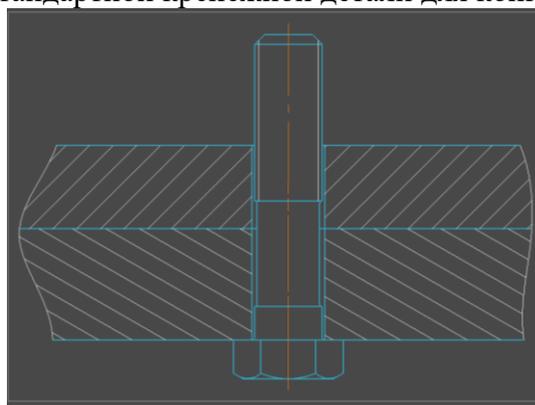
б – Внесение готовой стандартной крепежной детали в узел
